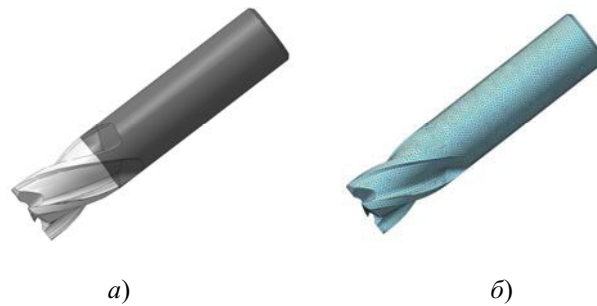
3D модель фрезы (а) и конечно-элементная сетка (б)
